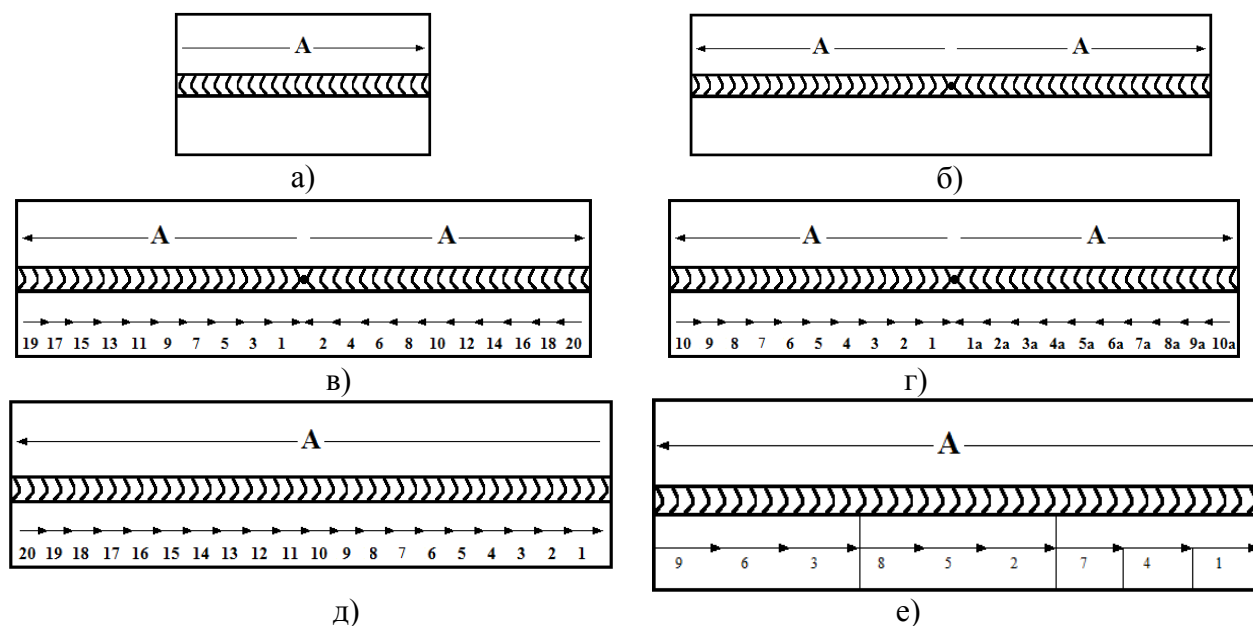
Схема сварки швов различной протяженности
